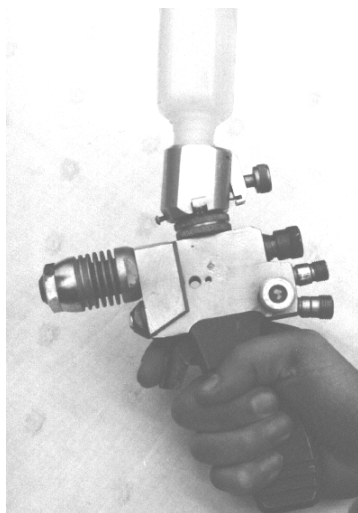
Газопламенная горелка для порошкового напыления «Искра-1»
